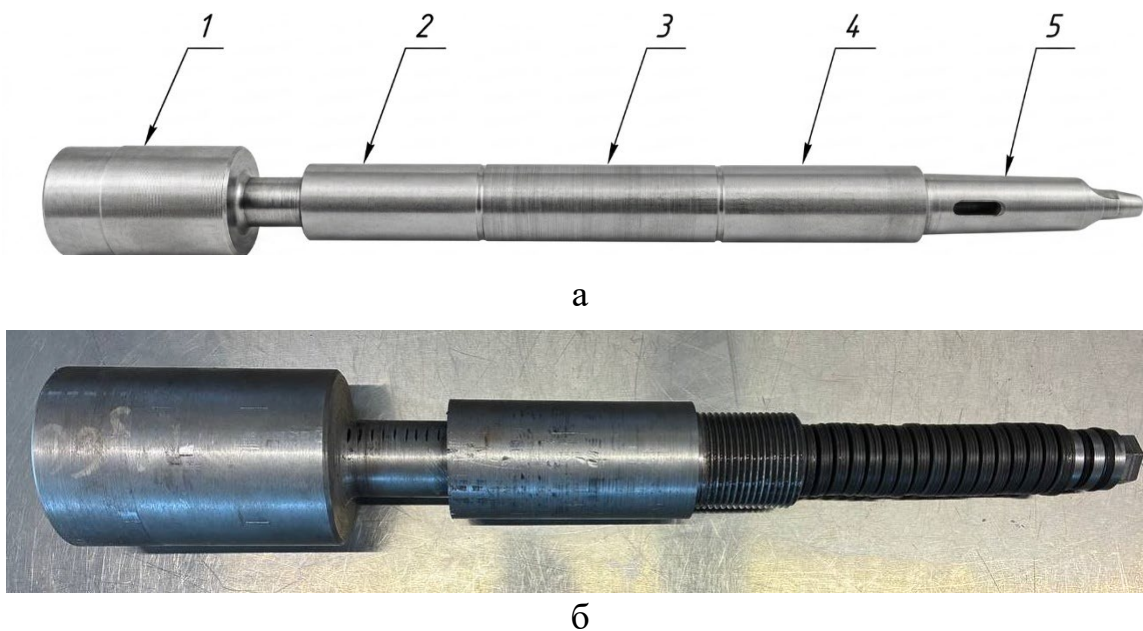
Лабораторний взірець амортизатора: а – зовнішній вигляд; б – внутрішні компоненти; 1 – вихідний вал; 2 – різбовий корпус; 3 – пружинний корпус; 4 – верхній перехідник; 5 – конус Морзе для встановлення у шпиндель верстата 2A554
